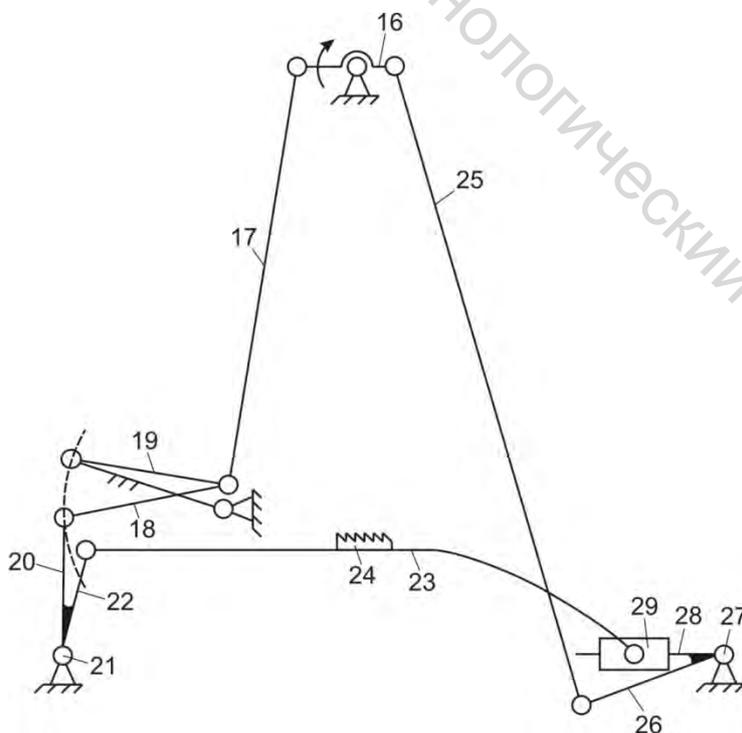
Регулировка длины стежка и обратного хода
